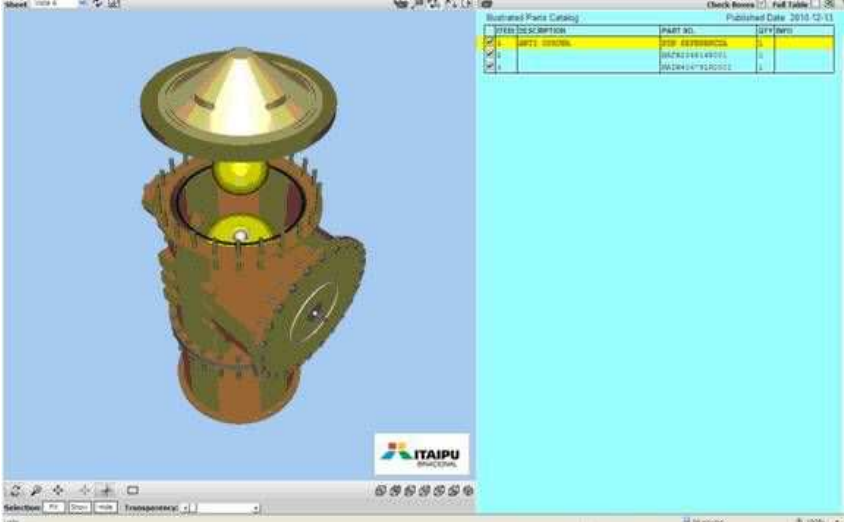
Protótipos de CV3D com vista explodida para a seccionadora
